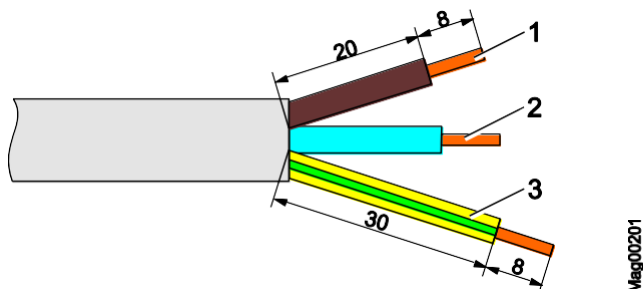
Isolar o cabeamento de rede elétrica (dimensões em mm)
